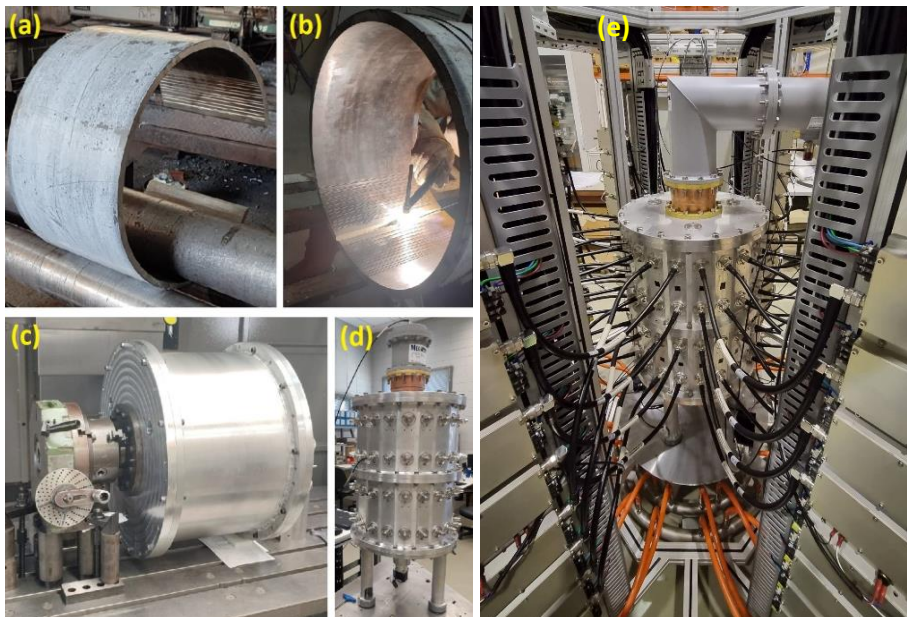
Processo de fabricação da cavidade combinadora: (a) calandragem, (b) soldagem, (c) usinagem, (d) montagem para testes em baixa potência e (e) montagem para testes de alta potência.
